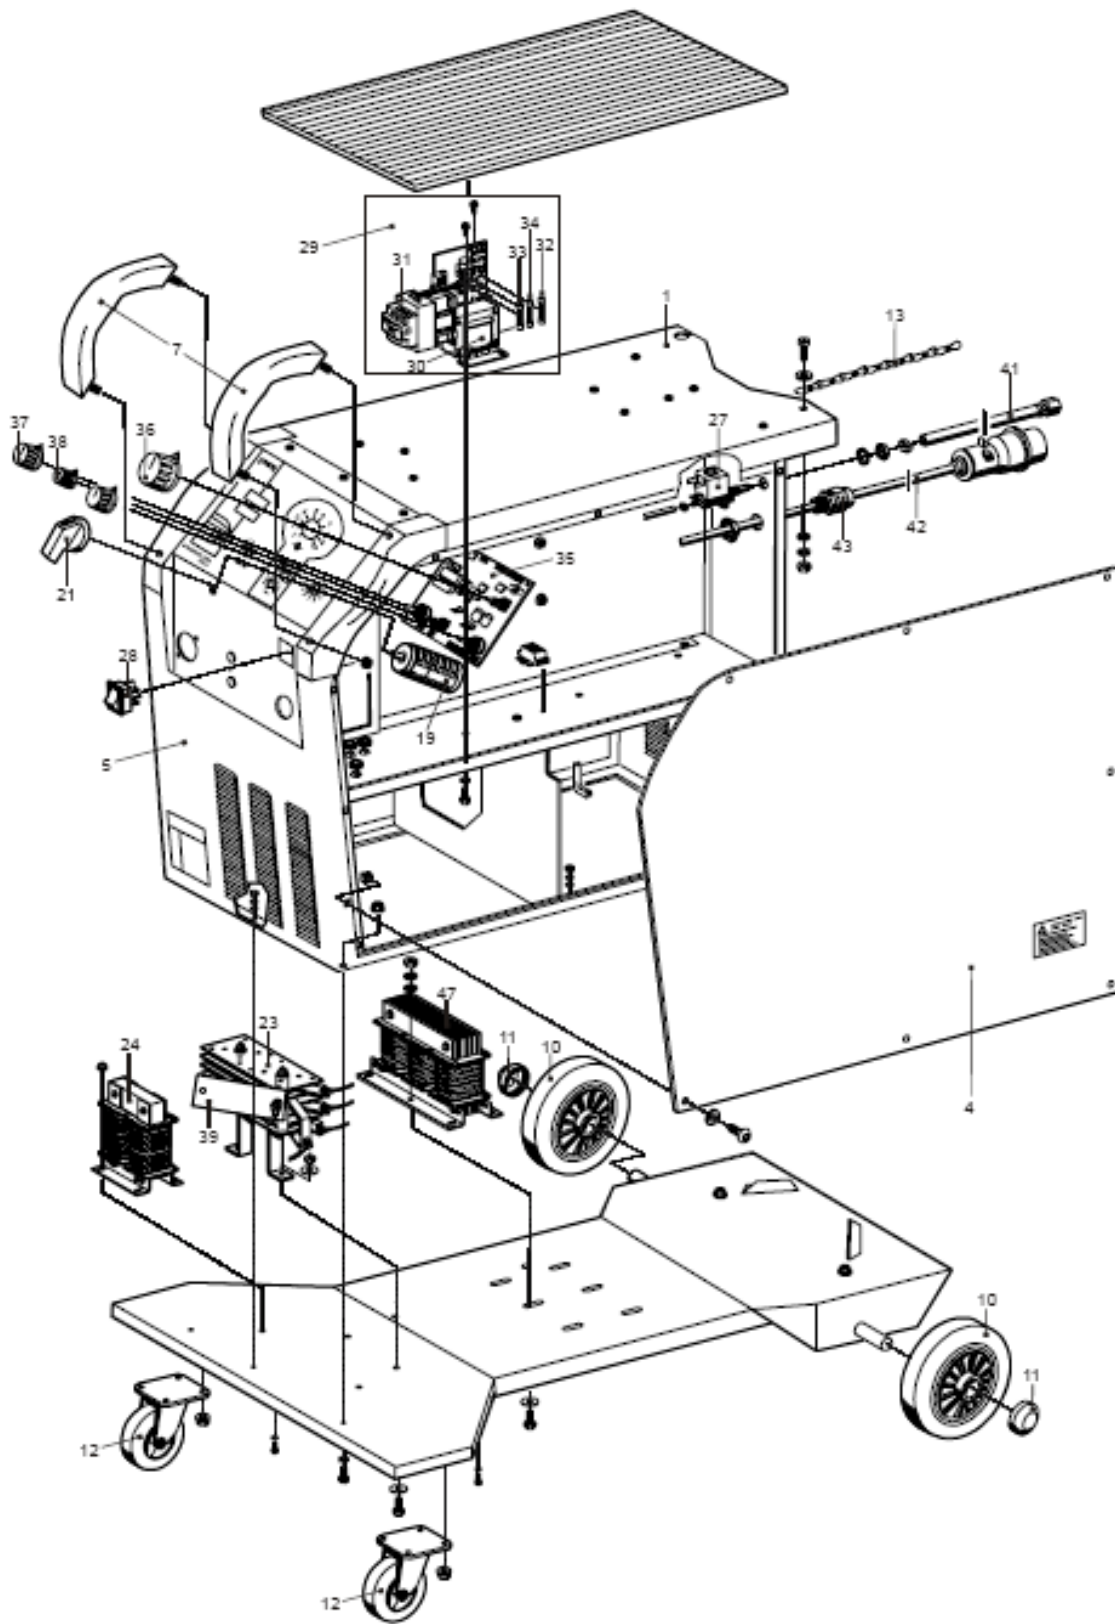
explosietekening Emigma 250-4 ÷ 450-4W (rechts)
